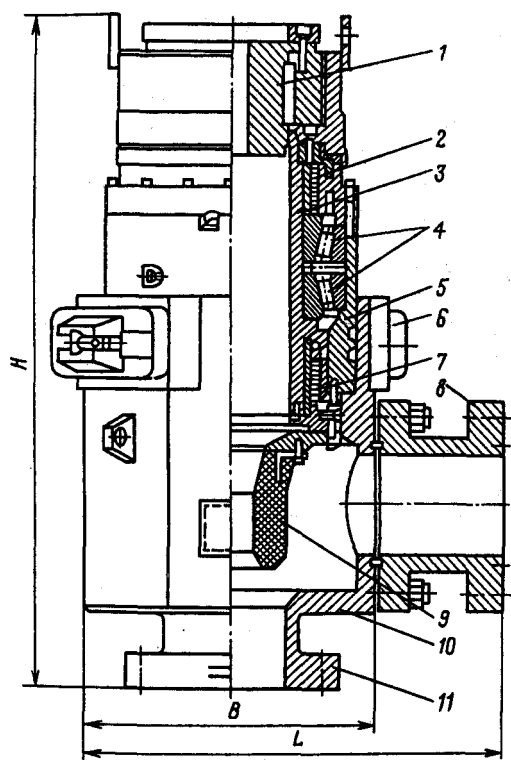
Роторный герметизатор ЦКБ "Титан":
